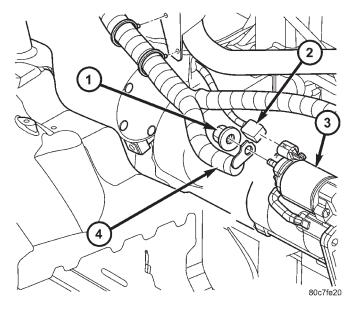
CONECTORES ELECTRICOS DEL MOTOR DE ARRANQUE - MOTOR 2.5L DIESEL
